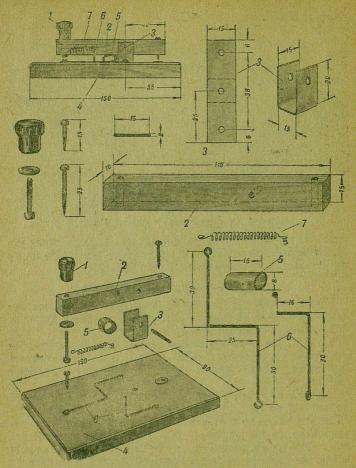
Ключ: 1—ручка (клемма от радиоприемника), 2—деревянный рычаг, 3—подшипник рычага, 4— основание, 5—пружинка (обрезок резиновой трубки), 6—жесткие соединительные провода, 7—гибкий соединительный провод.
